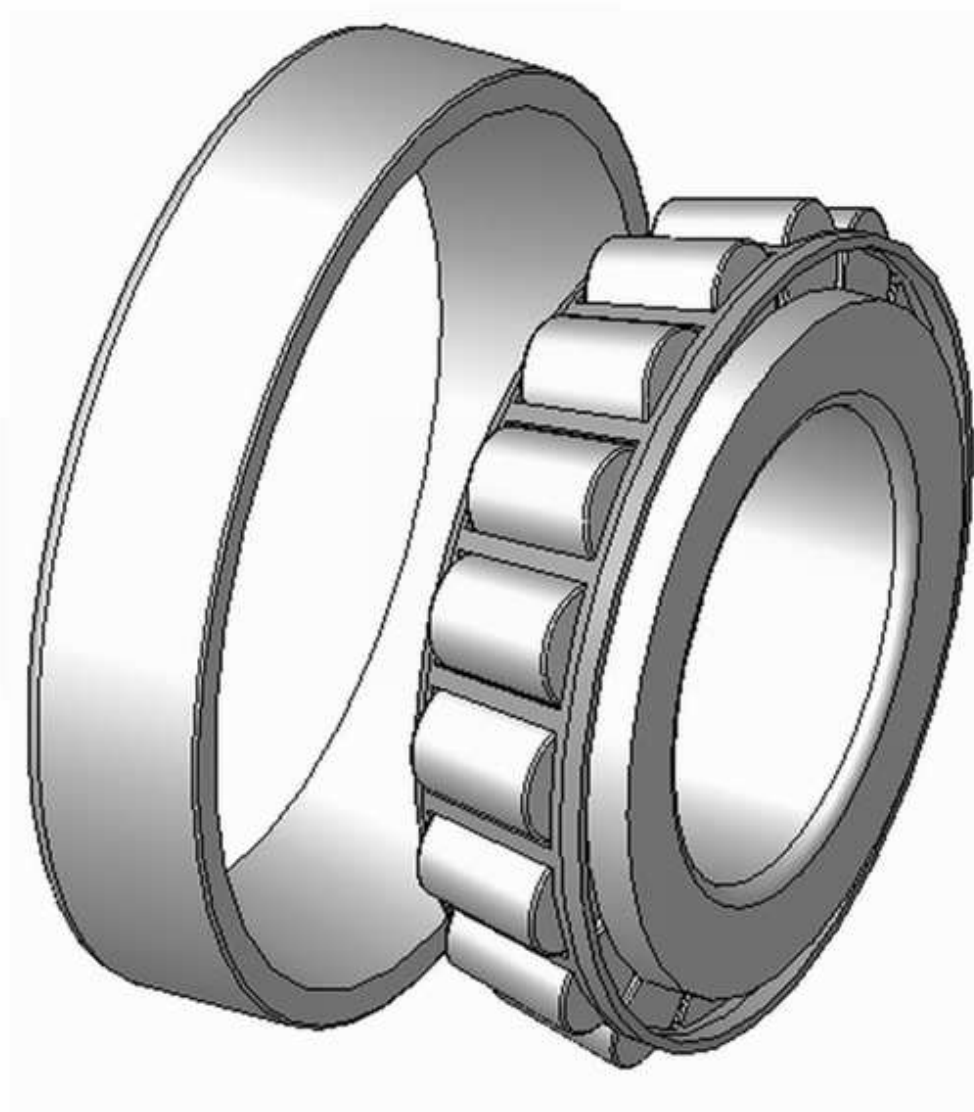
Роликовый конический подшипник с упорным бортом
